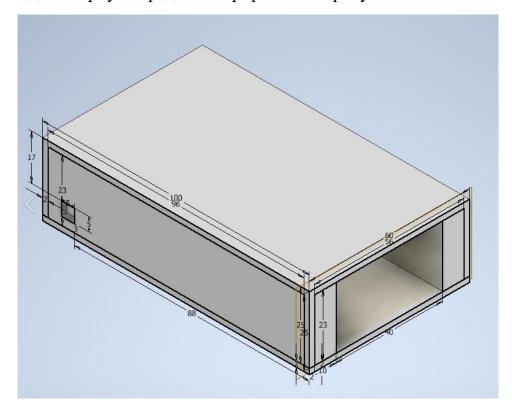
3D-модель корпуса ультразвукового дальномера
